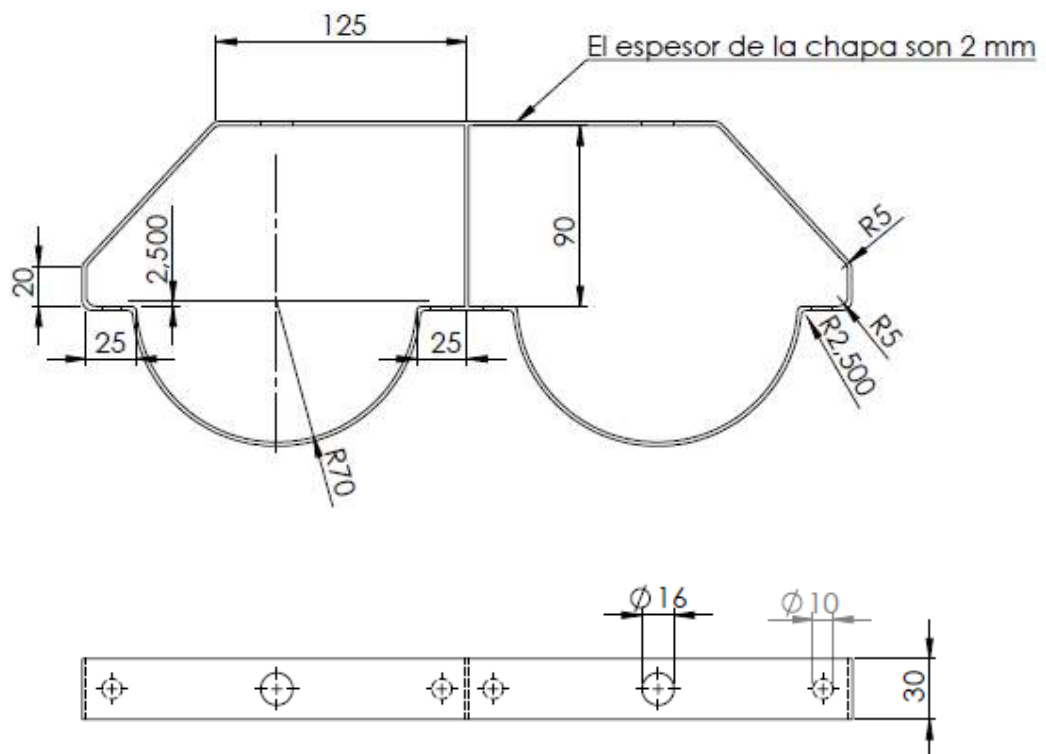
Plano estructura de sujeción. (Fuente: Elaboración propia)
